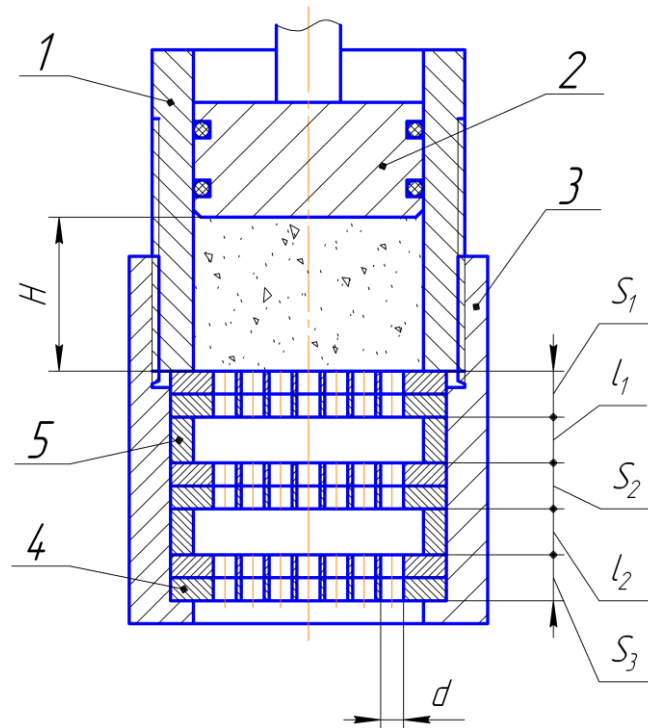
Схема робочої камери пристрою для вимірювання ГО РВ вовчків:
